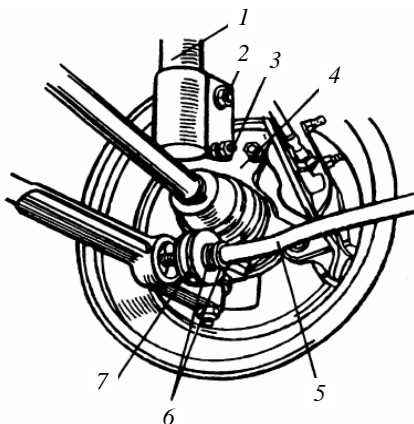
Вариант регулировки геометрического положения колёс автомобиля с подвеской типа «качающаяся свеча»:
